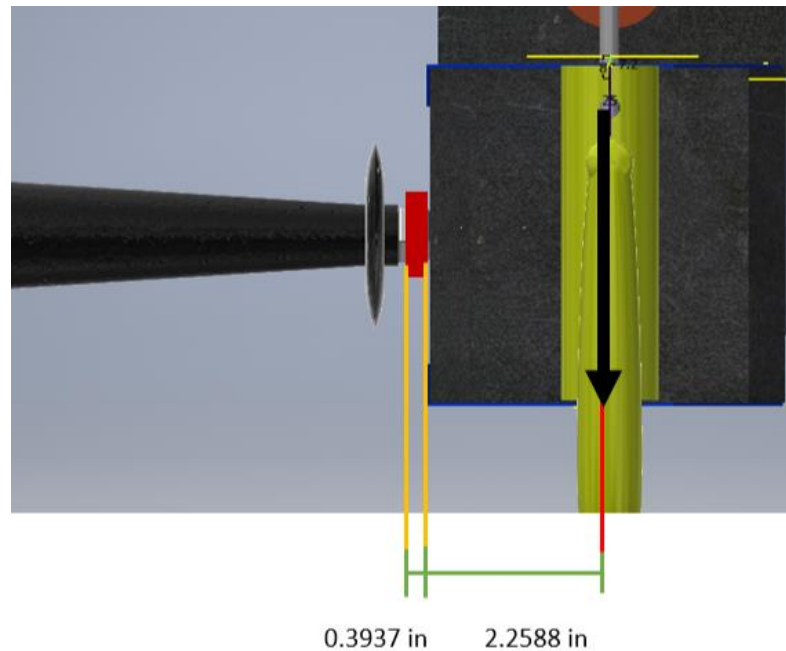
DLC de la Distribución de Fuerzas para soldadura
